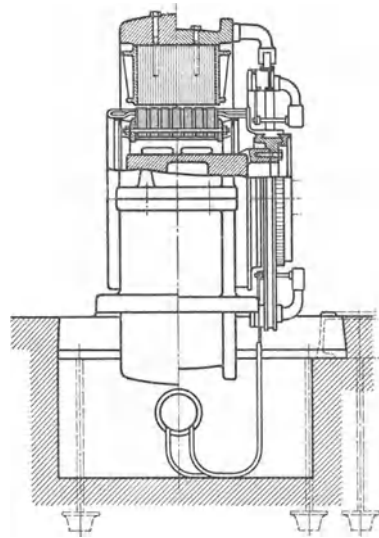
Gleichstromgenerator ohne Welle und Lager für Zusammenbau mit Kolbendampfmaschine.
